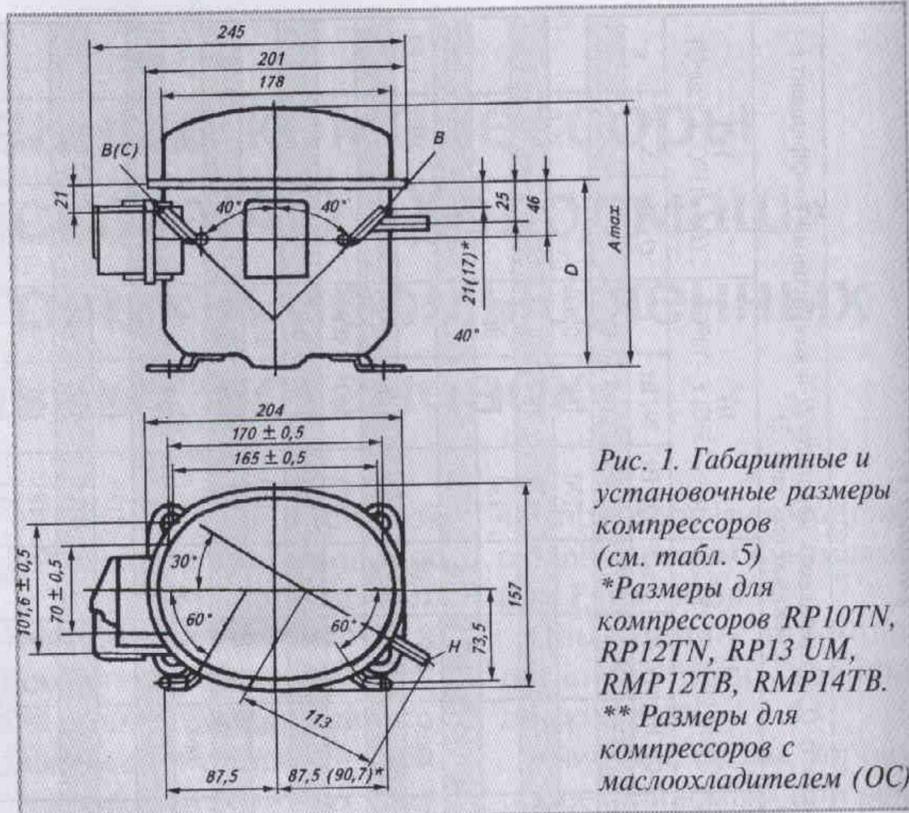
Габаритные и установочные размеры компрессоров (см. табл. 5)
